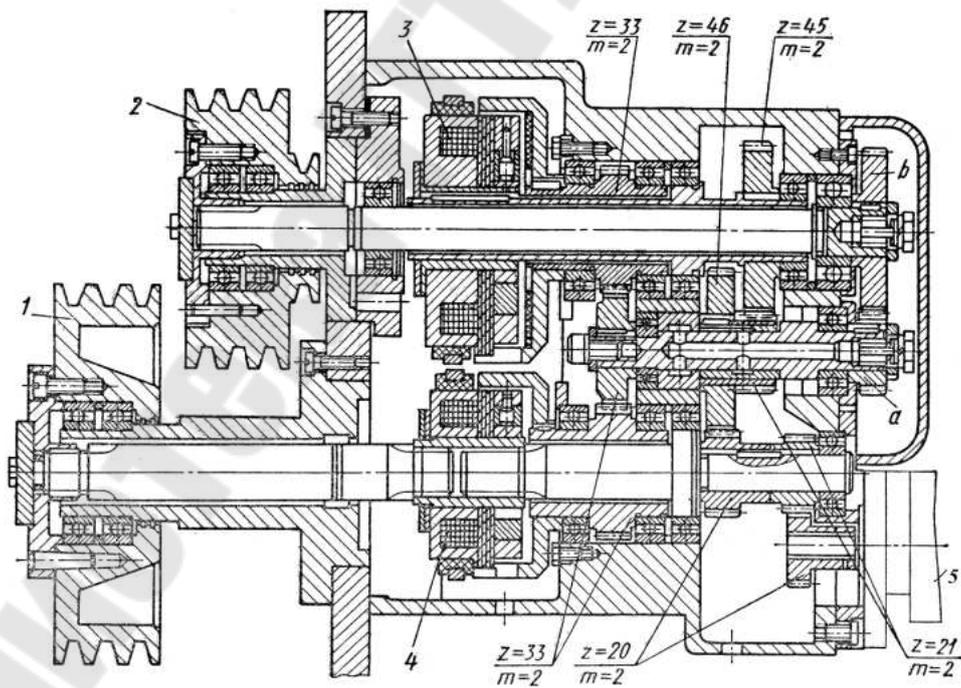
Коробка скоростей револьверного станка модели 1Н318:
